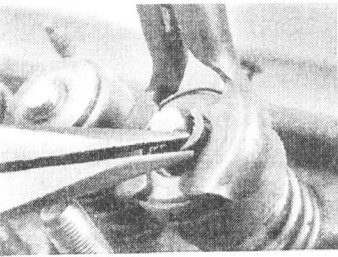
Сжать пружину клапана рассухаривателем и снять сухари с помощью небольшого магнита или пинцета.
